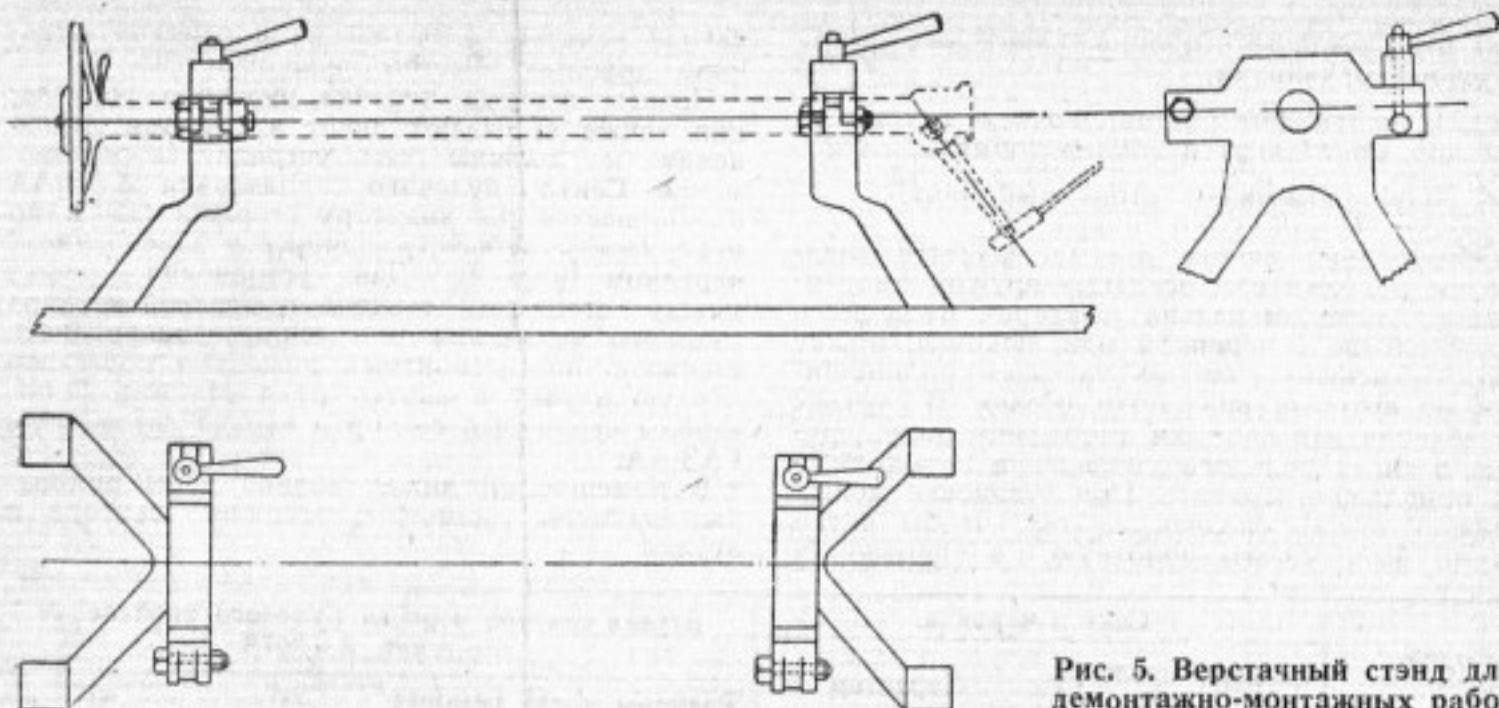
Верстачный стенд для демонтажно-монтажных работ
